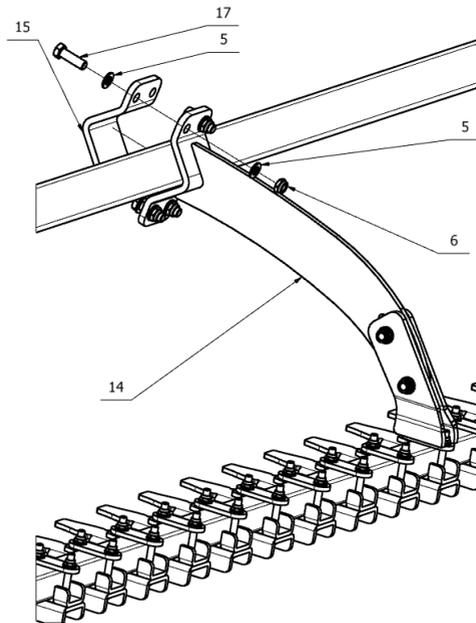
T-Welle Ø600mm - obere Befestigung der Mittelhalterung.
